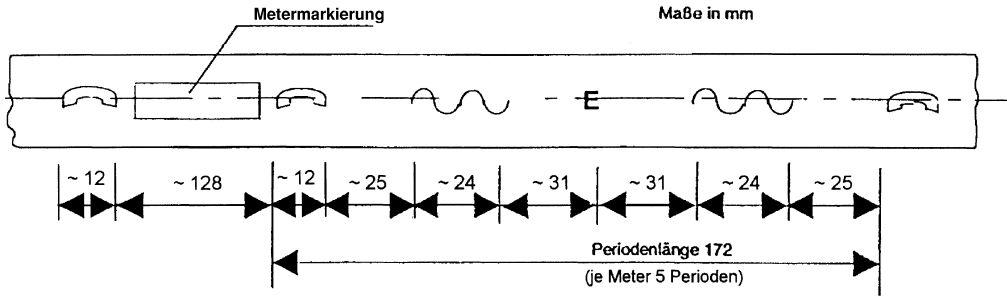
Äußere Kennzeichnung für Kabel mit Einmodenfaser
